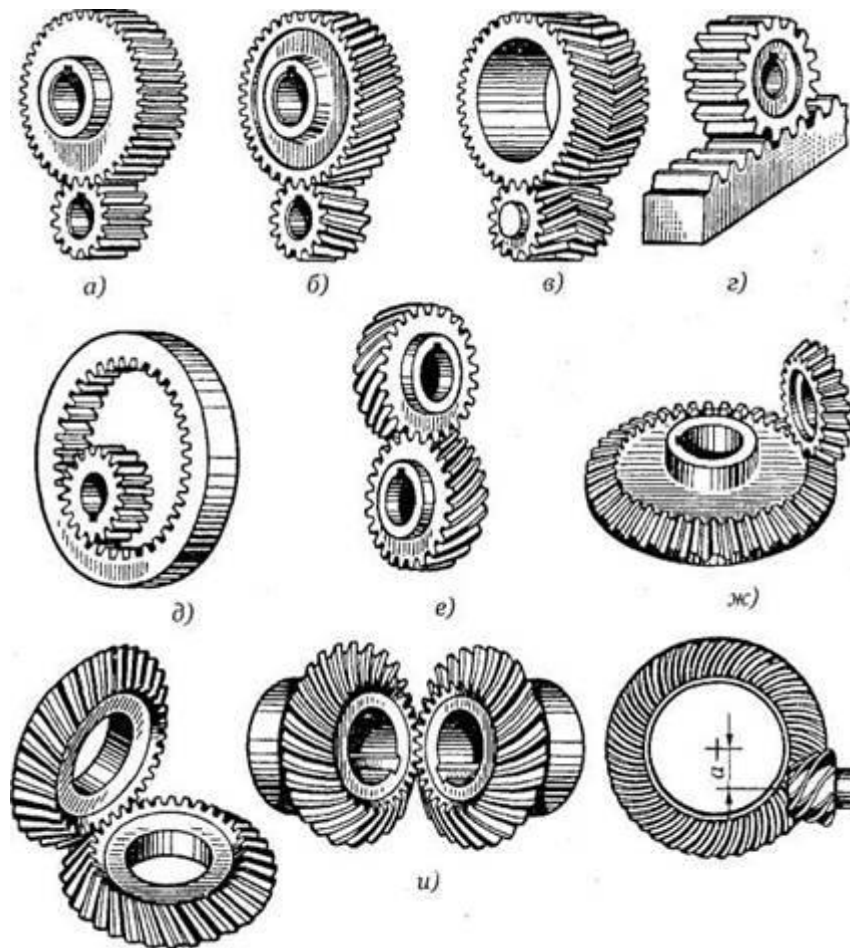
Основні види зубчастих передач: а, б, в – зовнішня циліндрична прямозуба, косо зуба та шевронна, г – передача шестерня-рейка, д – циліндрична передача з внутрішнім зачепленням, е – зубчаста гвинтова передача, ж, з, и – зубчасті конічні передачі прямозуба, косозуба, з криволінійним зубом, к – гепоїдна передача
